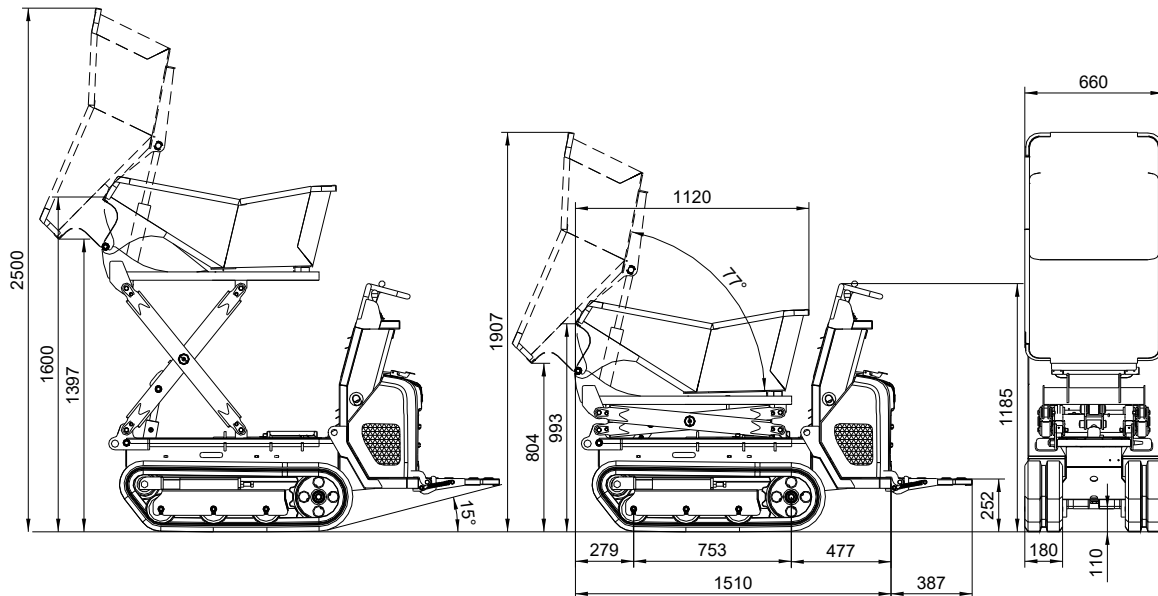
Dimensions de la machine (modèle DT05-P avec benne basculante vers le haut)
